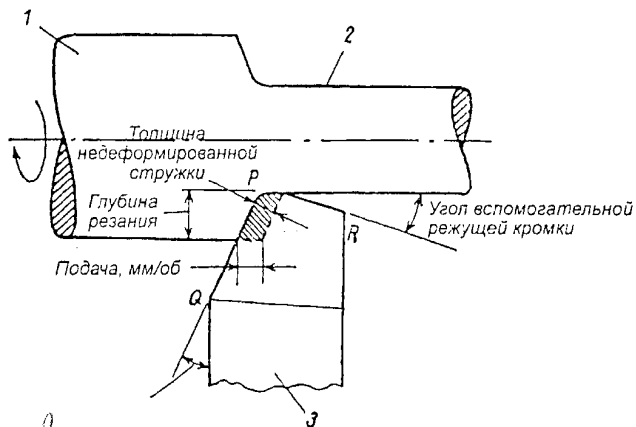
Дополнительные данные об основных элементах и исходных поверхностях однолезвийного резца. Р – вершина резца; РО – главная режущая кромка; РК – вспомогательная режущая кромка.
